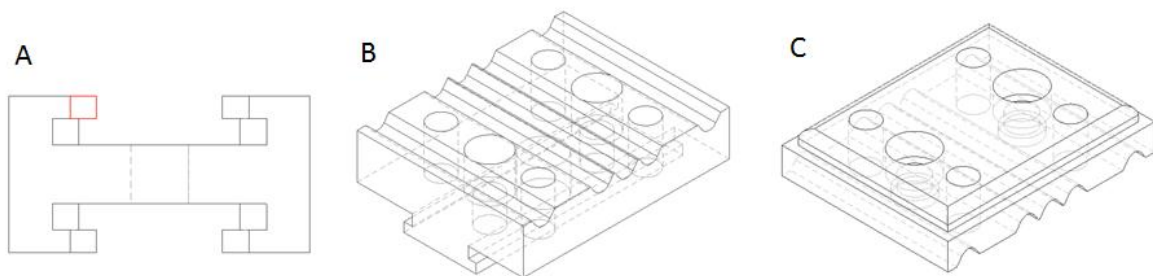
A SECCIÓN TRASVERSAL DEL RIEL, B FORMA DE LA PRENSA, C GEOMETRÍA DE LA TAPA.
